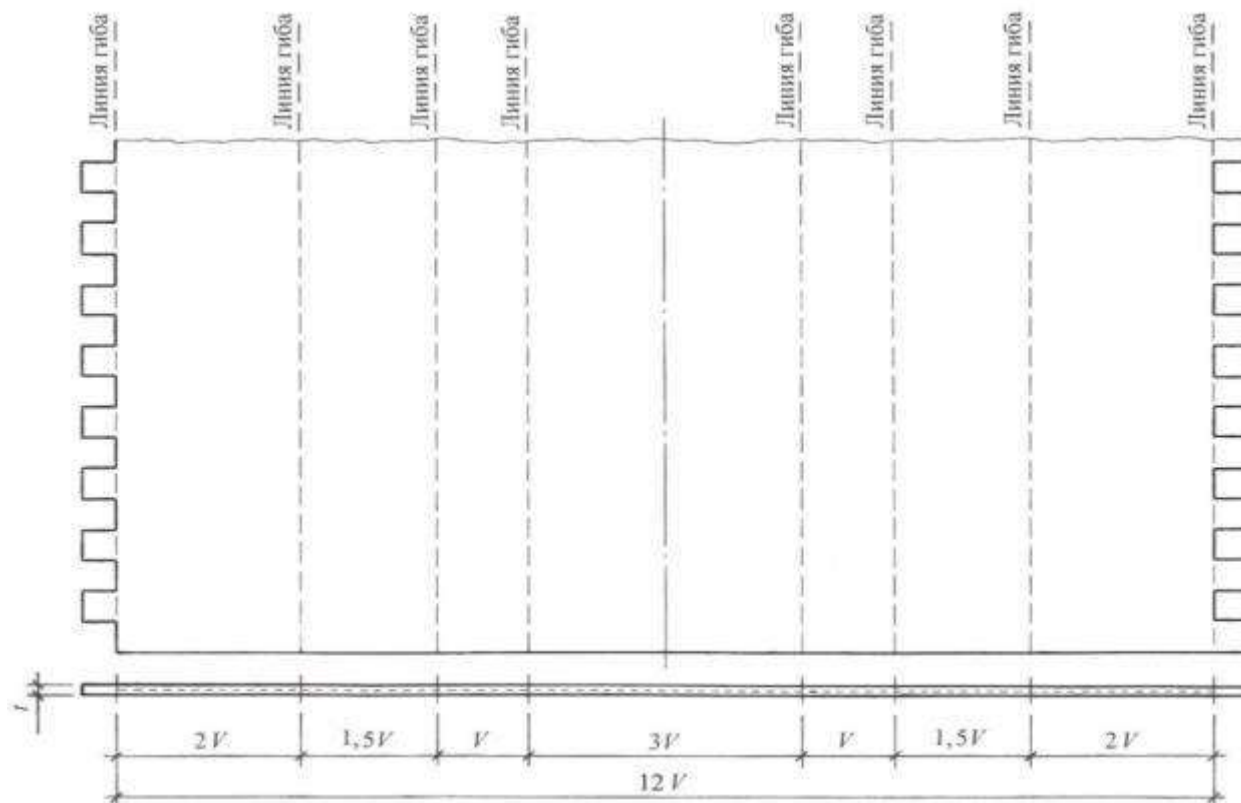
Развертка листовой заготовки (штрипса) с зубчатыми кромками для равноустойчивого профиля
